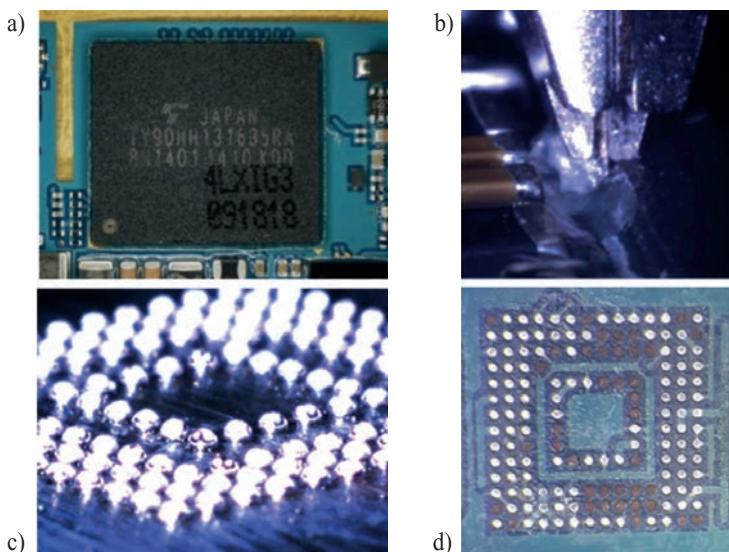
a) BGA-Bauteil auf der Leiterplatte, b) Einschneiden des Underfill am Rand des Bauteils, c) Bauteilunterseite nach dem Reballing, d) Leiterplattenoberfläche nach dem Reinigen – einige Pads wurden beim Auslötprozess abgerissen
